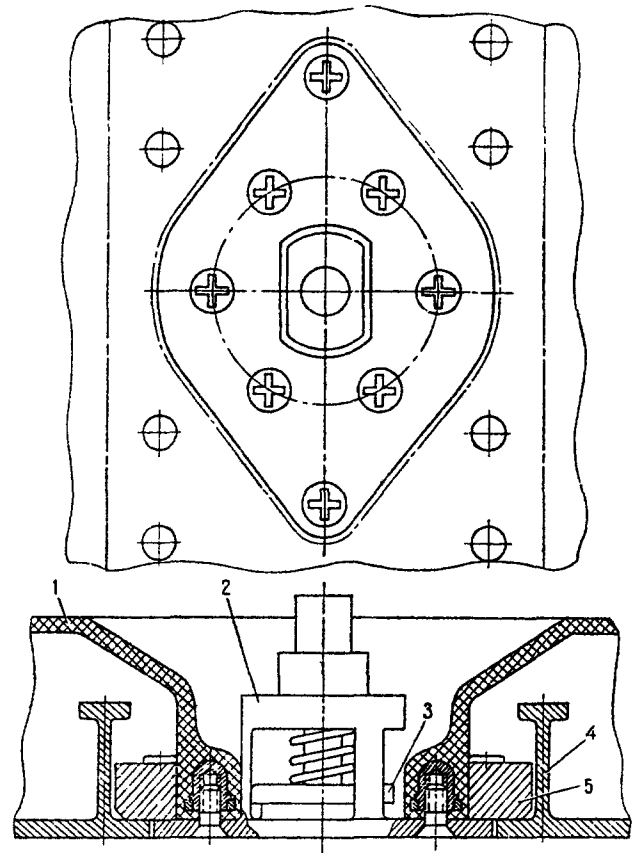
Установка поплавкового клапана в баке-отсеке
